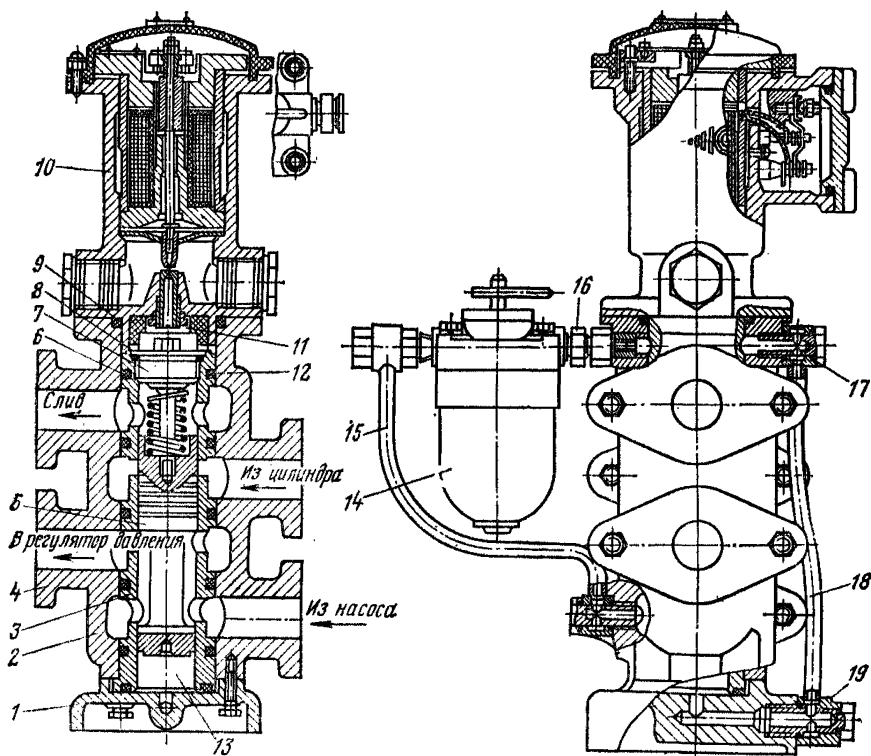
Устройство предохранительного торможения УПТВ:
